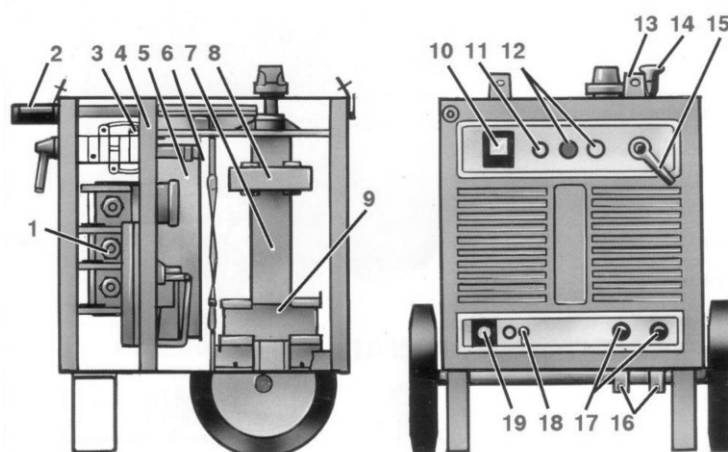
Внешний вид сварочного выпрямителя:
